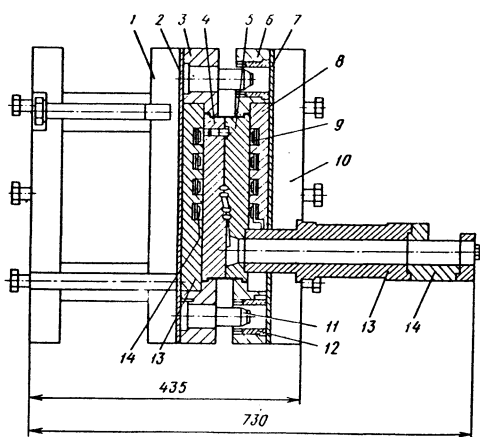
Блок-форма для литья стали под давлением: 1 - постамент; 2, 7 - экраны; 3, 6 - обоймы; 4, 5 - вкладыши из молибденового сплава; 8, 13 - плиты нагревателей; 9, 14 - нагреватели; 10 - плиты крепления; 11 - направляющая колонка; 12 - втулка; 13 - камера прессования; 14 - вставка из молибденового сплава
